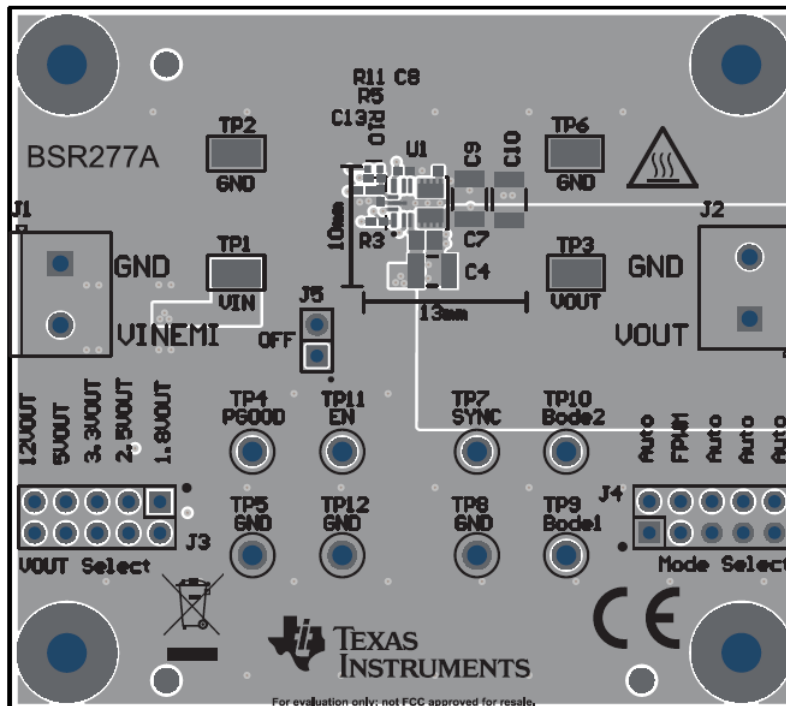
PCB 顶层 2D (TPSM365R15FEVM)
